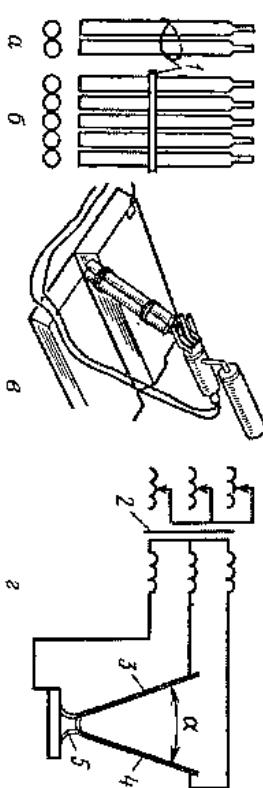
Схема сваренного электрода (а), гребенки (б) и сварки трехфазным током (в, г):
